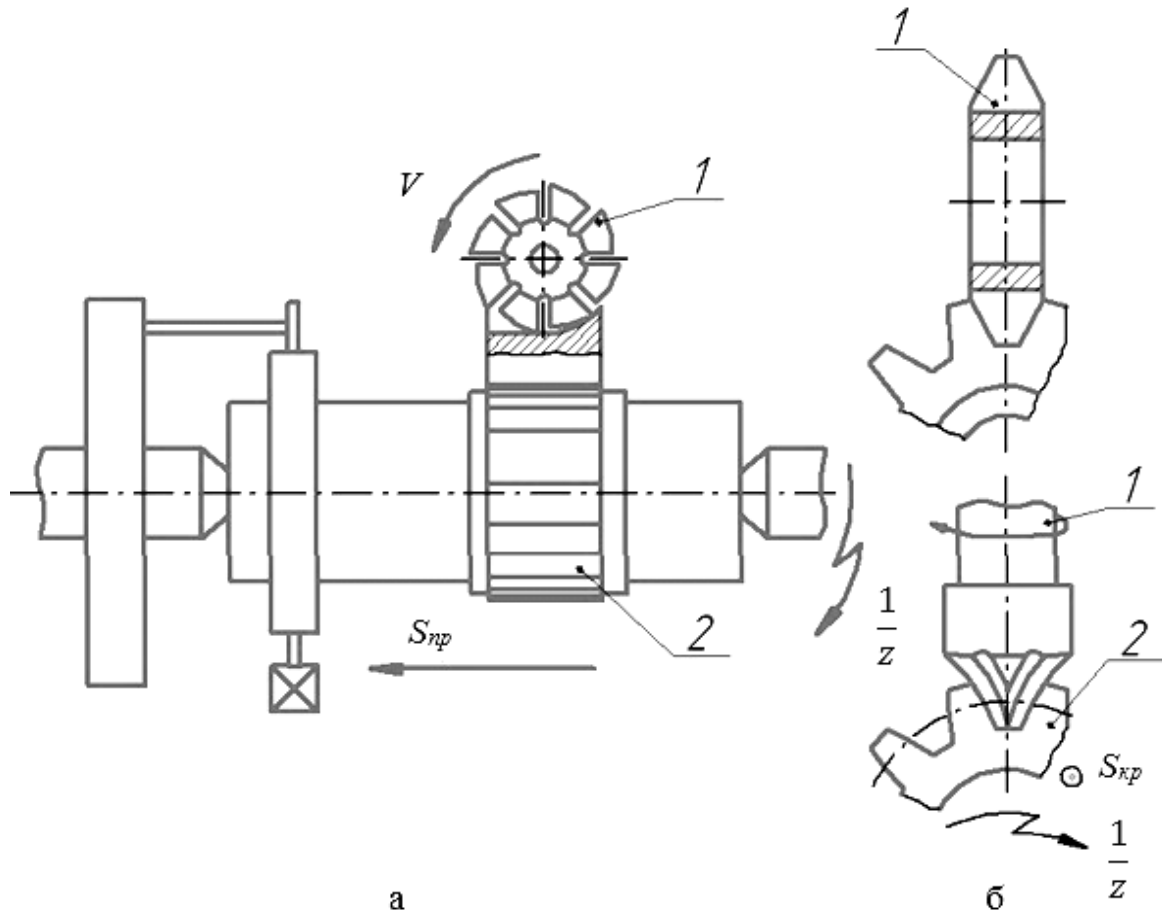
Схеми фрезерування зубів за методом копіювання
